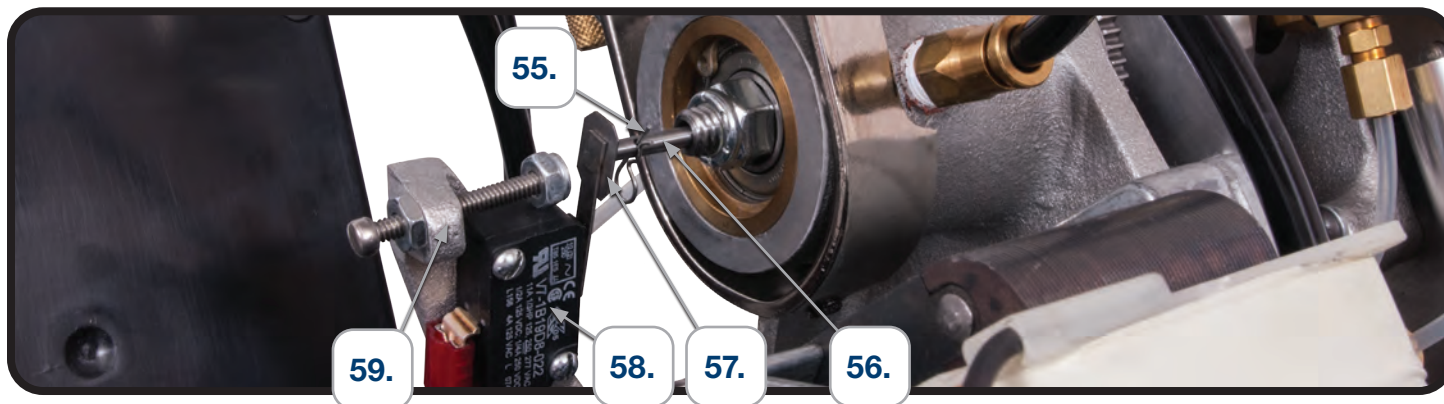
ENSEMBLE DE PLAQUE FRONTALE – VUE ARRIÈRE GAUCHE
